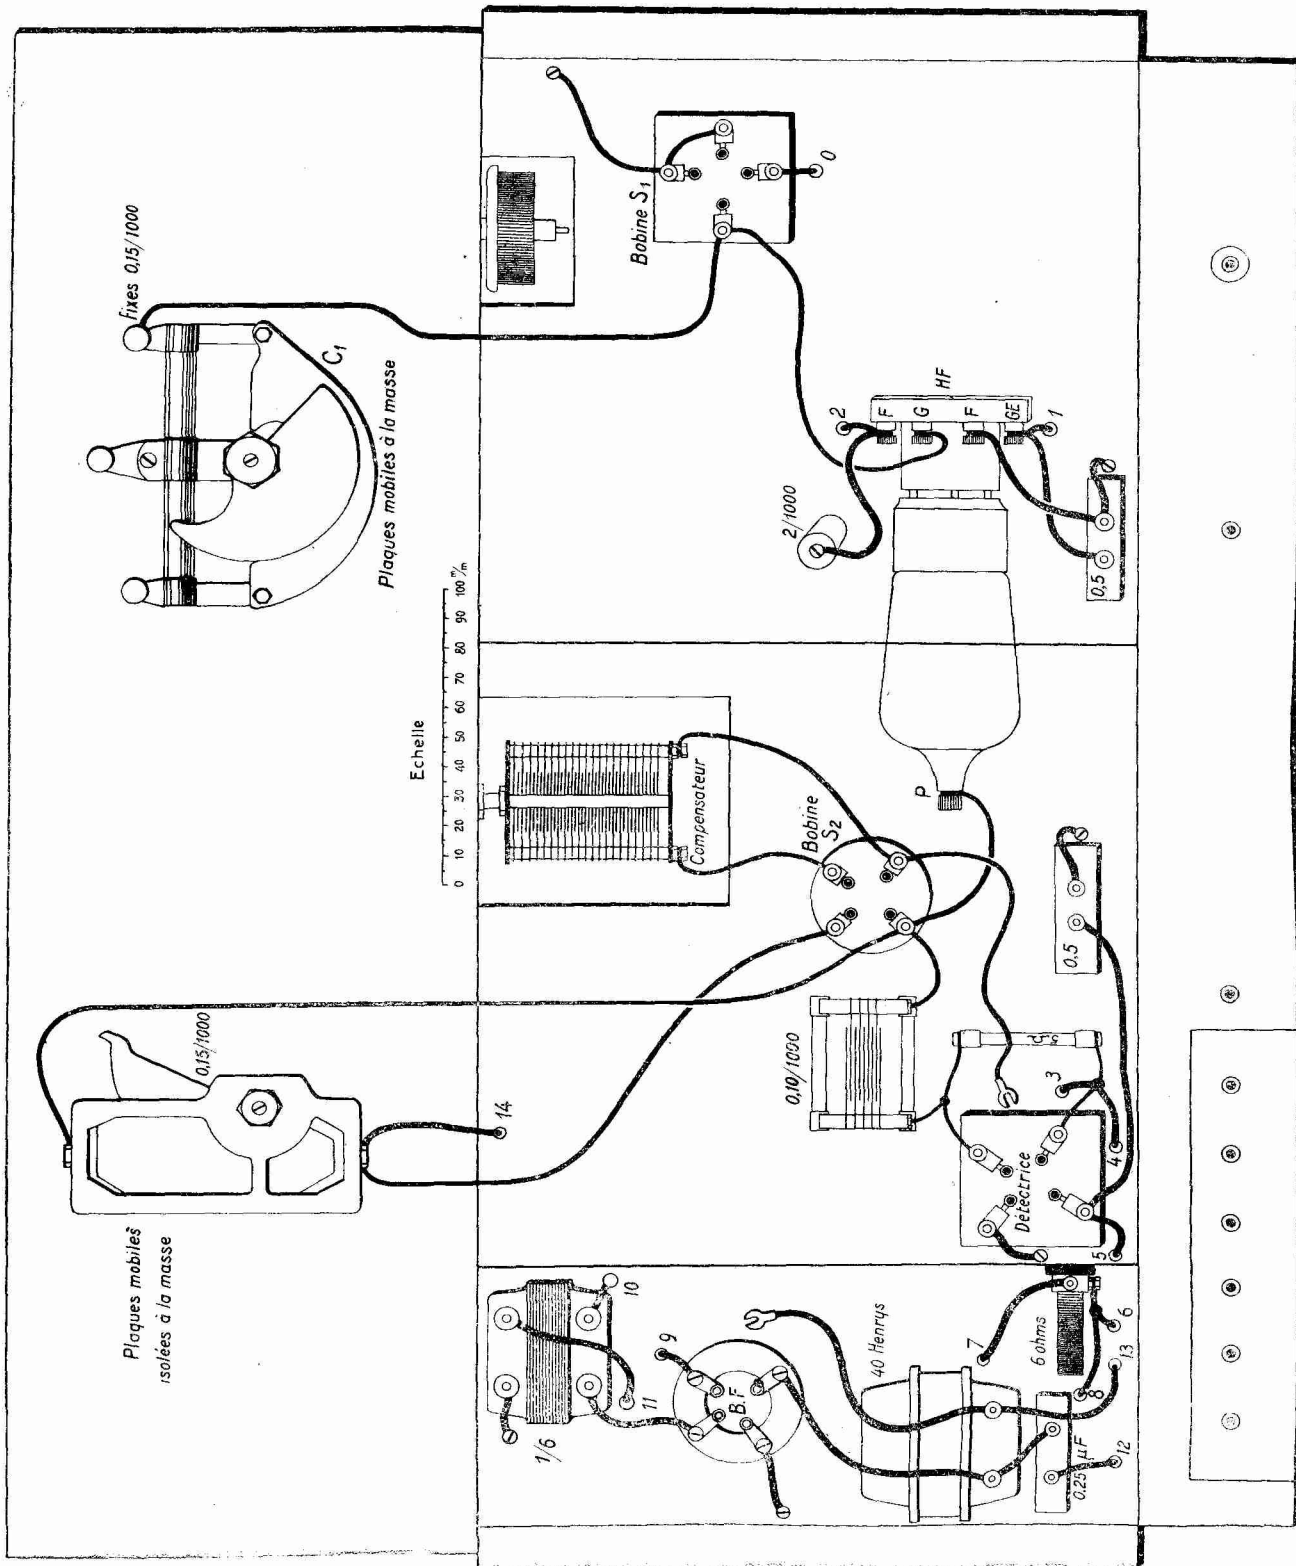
Plan des connexions disposées au-dessus du panneau horizontal
